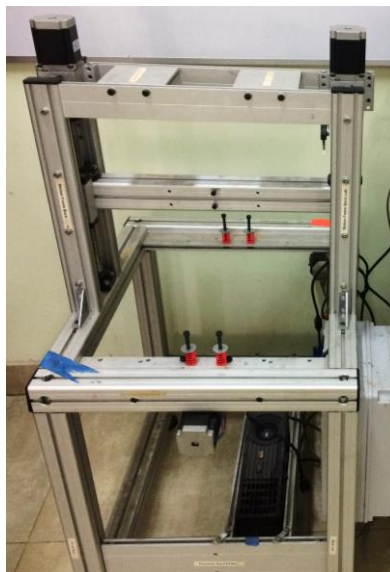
Impresora ILIOS 3D printer ensamblada.
